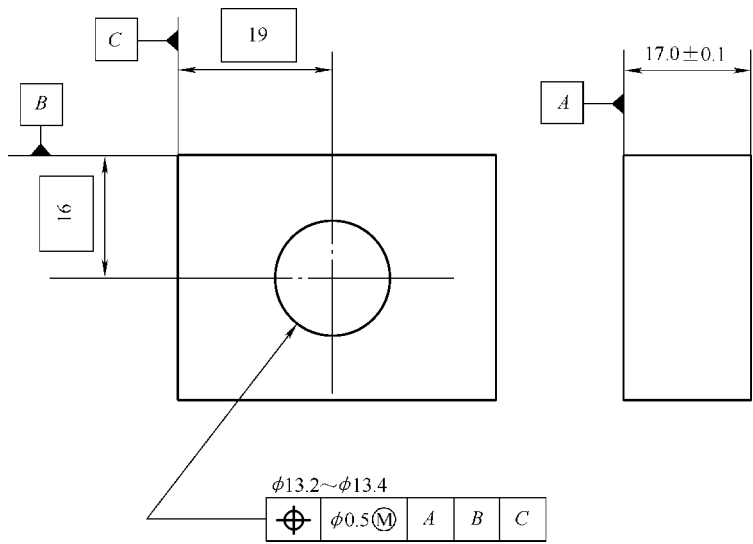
一个使用 MMC 修正的几何公差控制零件
